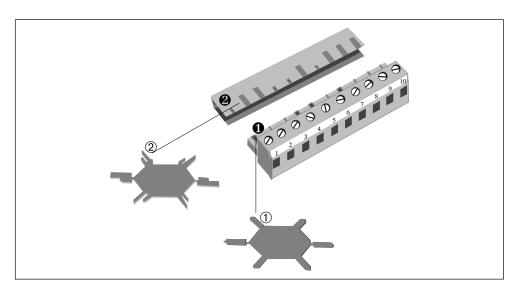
So werden Stecker unvertauschbar gemacht.
